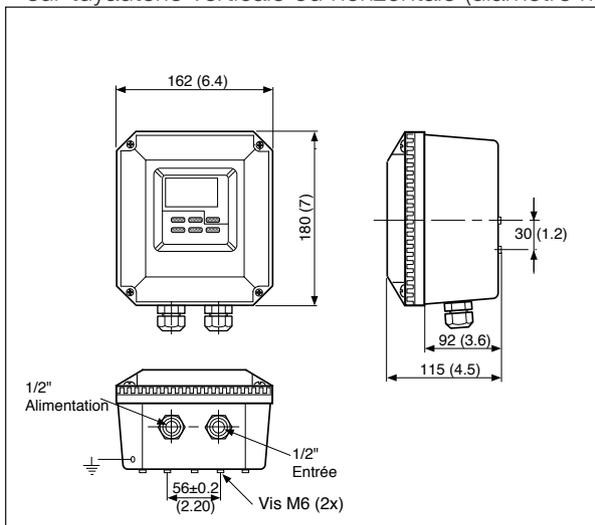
Dimensions de l'ensemble, emplacement des presse-étoupe
